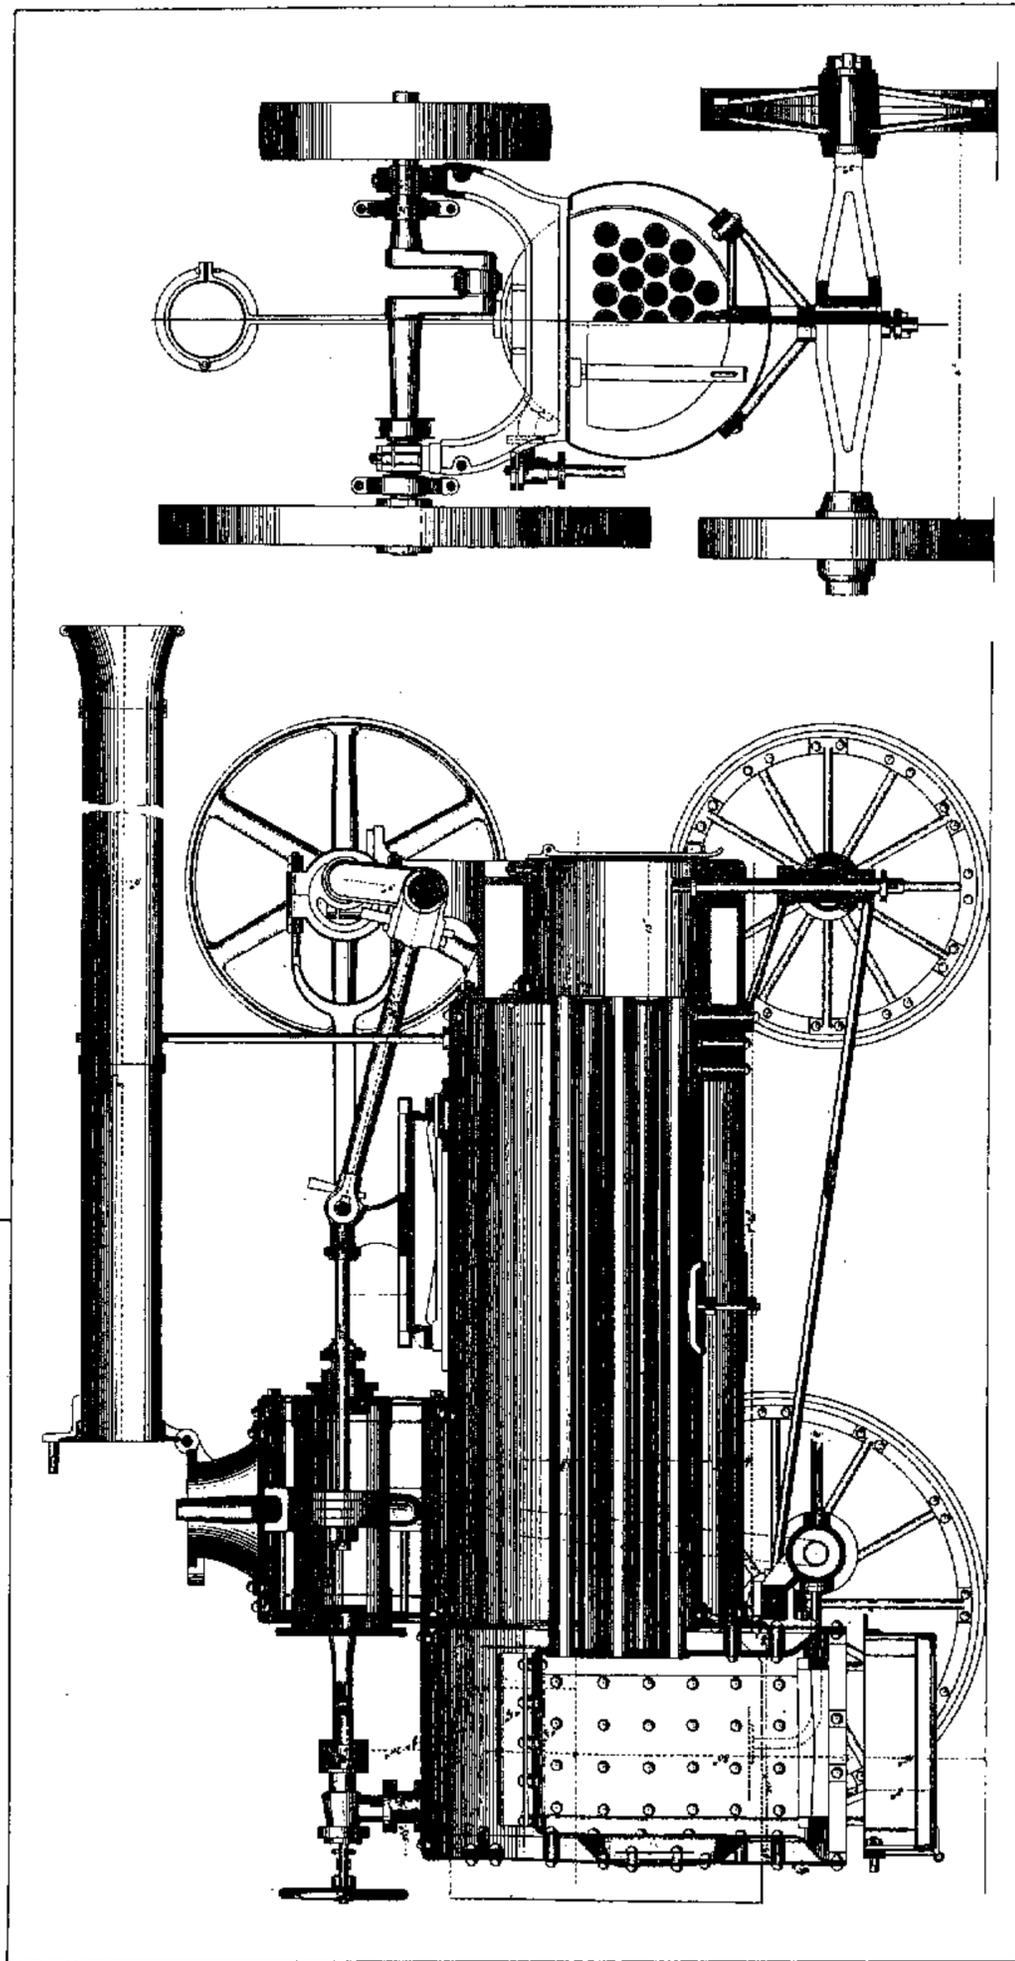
/2: Ausführung einer Klein-Dampfmaschine der Maschinenfabrik Esslingen mit unten seitlich abgehendem Kamin (um 1888)
